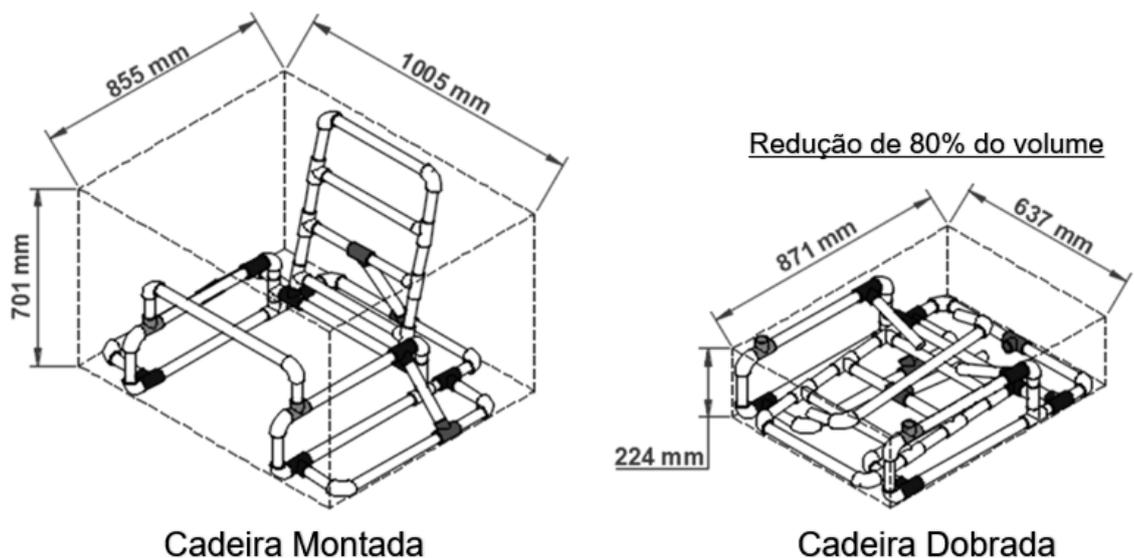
Desenho esquemático do instrumento montado e dobrado.
